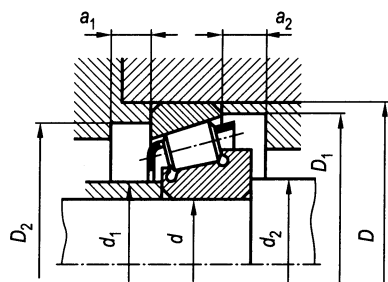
Установочные размеры для роликового радиально-упорного конического однорядного подшипника
